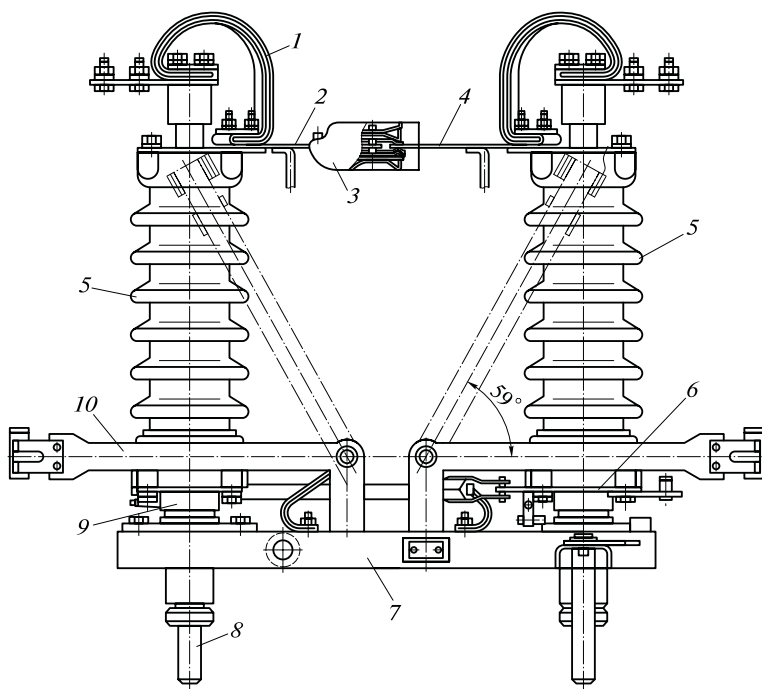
Общий вид разъединителя типа РЛНД-35:
